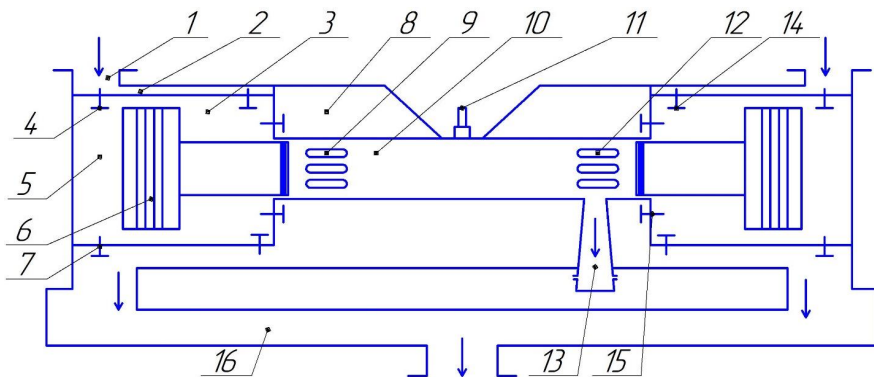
Общая схема одноступенчатого свободнопоршневого компрессора
